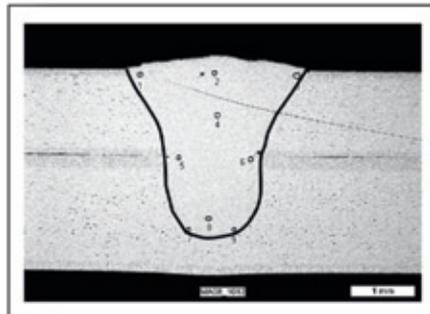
Heißrissfreie Remote-Laser-Schweißnaht mit zwei „Novelis Fusion™“ Blechen.
